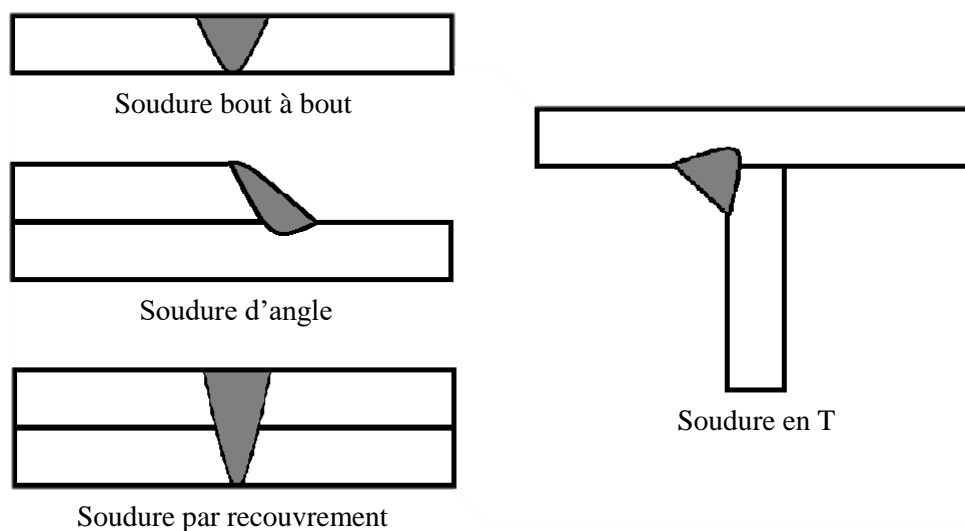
Types de configurations de soudures utilisées dans le soudage laser
